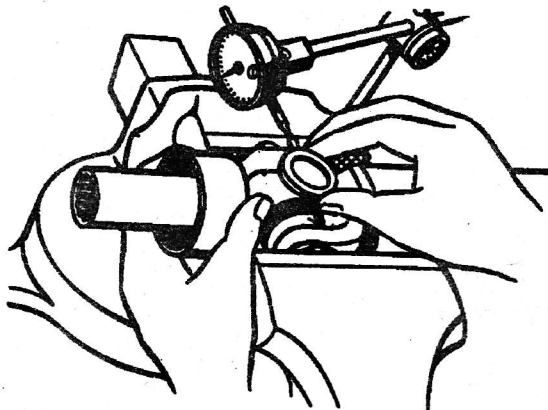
Измерение радиального зазора в подшипниках карданного шарнира
